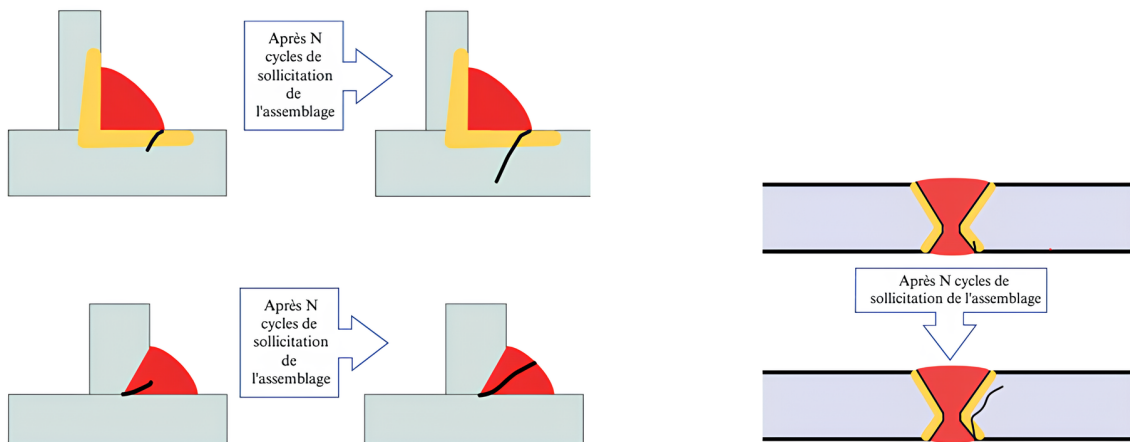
Localisation des fissures de fatigue dans les assemblages soudés [6].
